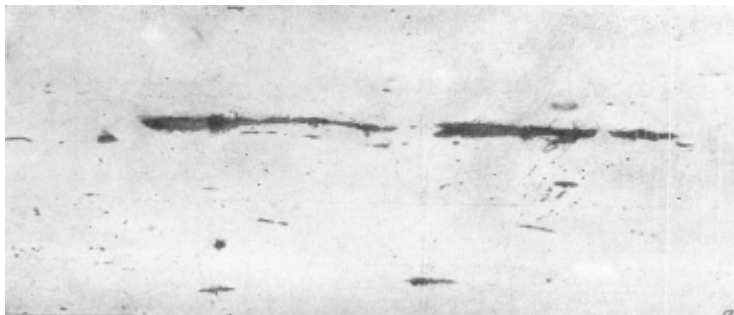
Неснятые брызги металла на сварном шве
